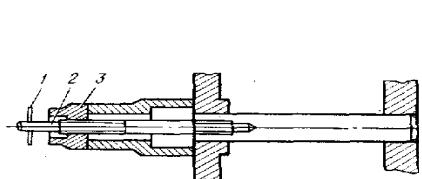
Съемник для выпрессовки оси блока шестерен заднего хода.
